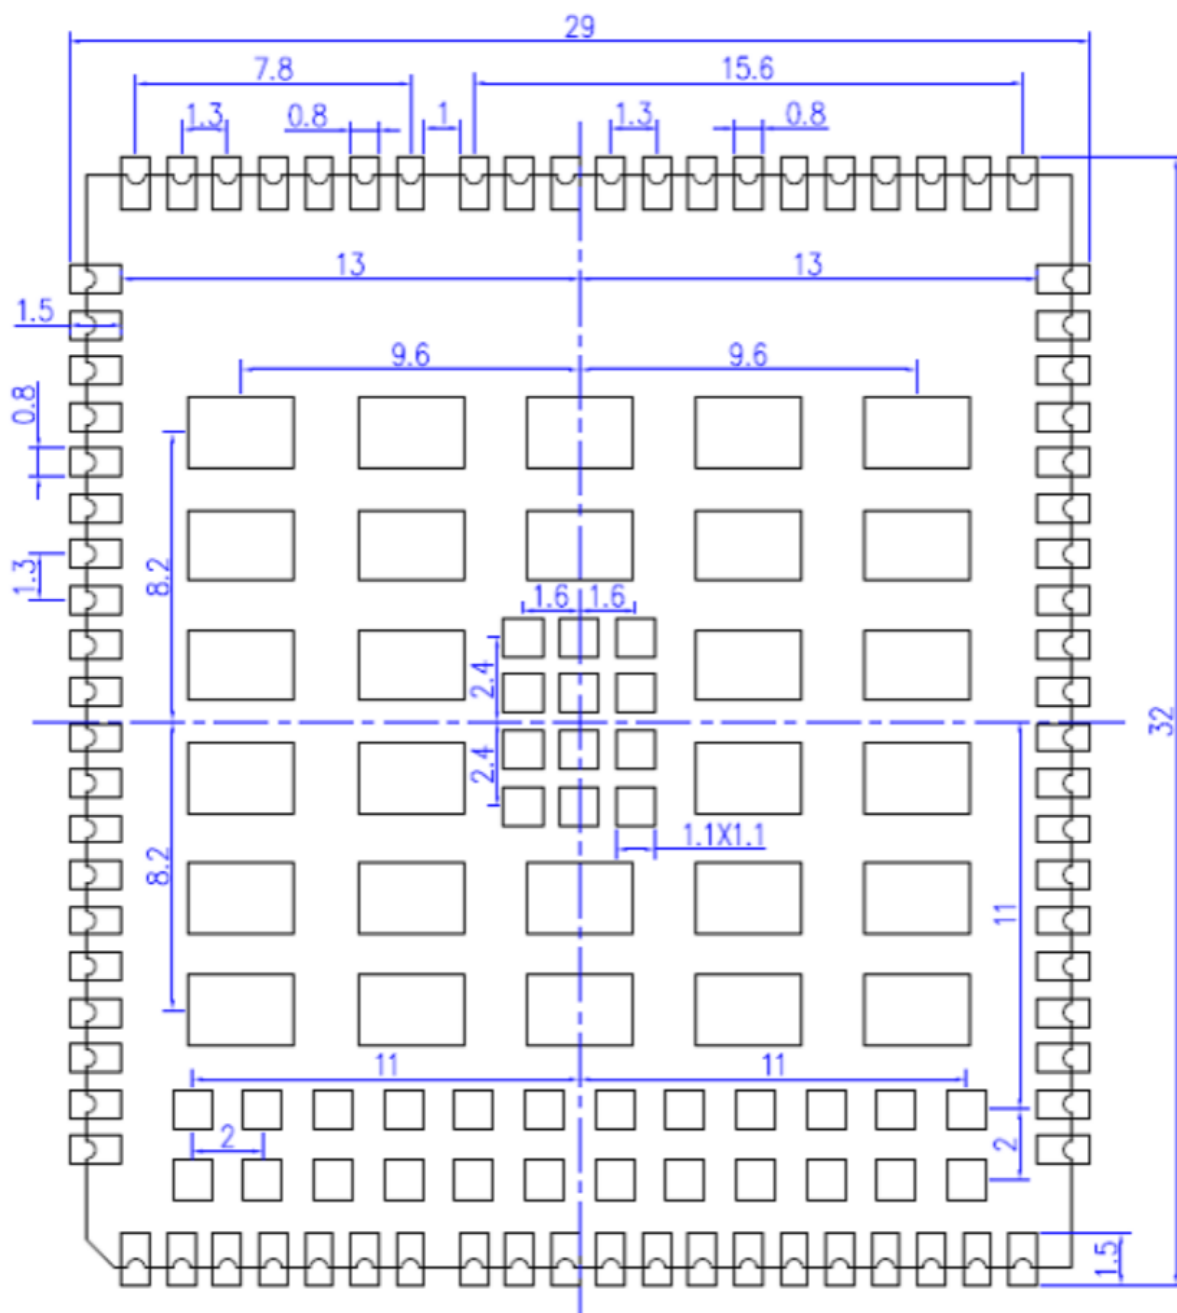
L610 PCB 焊盘设计 (单位: mm)
